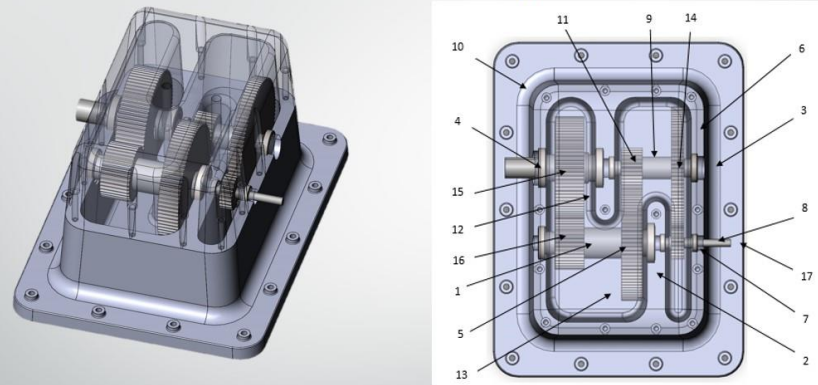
3Д-модель редуктора з нумерацією деталей:
